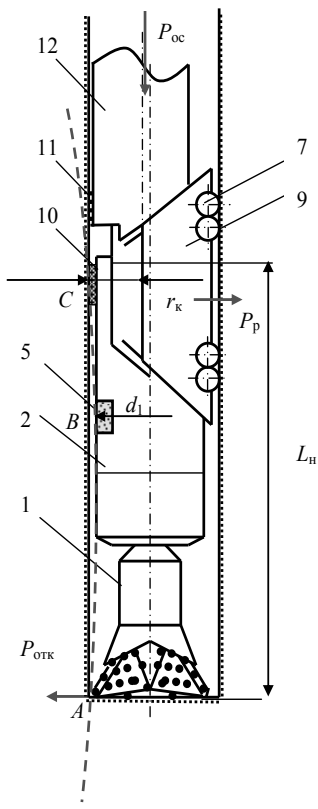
Схема отклонителя ТЗ-3П-59 в рабочем положении
